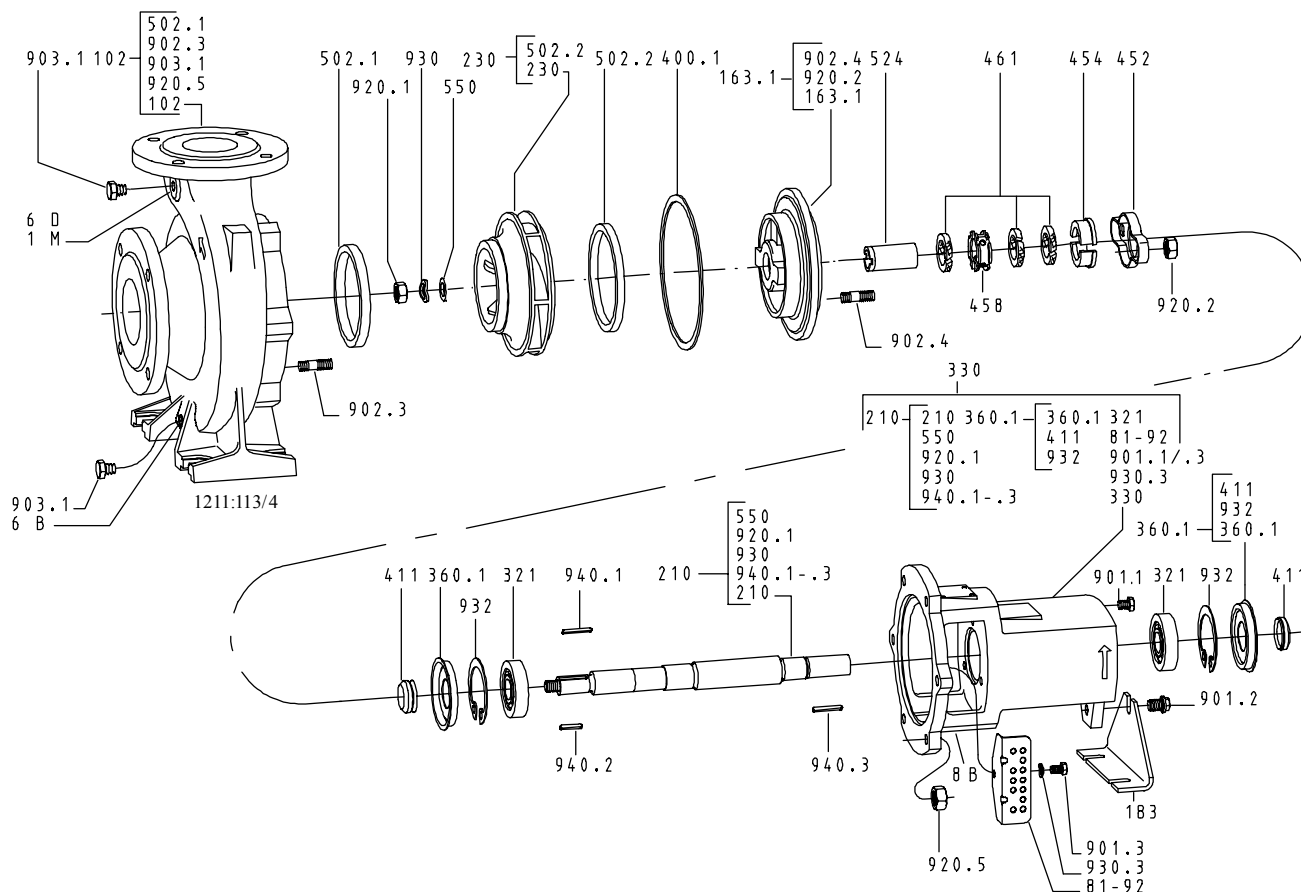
Сальниковая набивка и зажимная крышка корпуса
